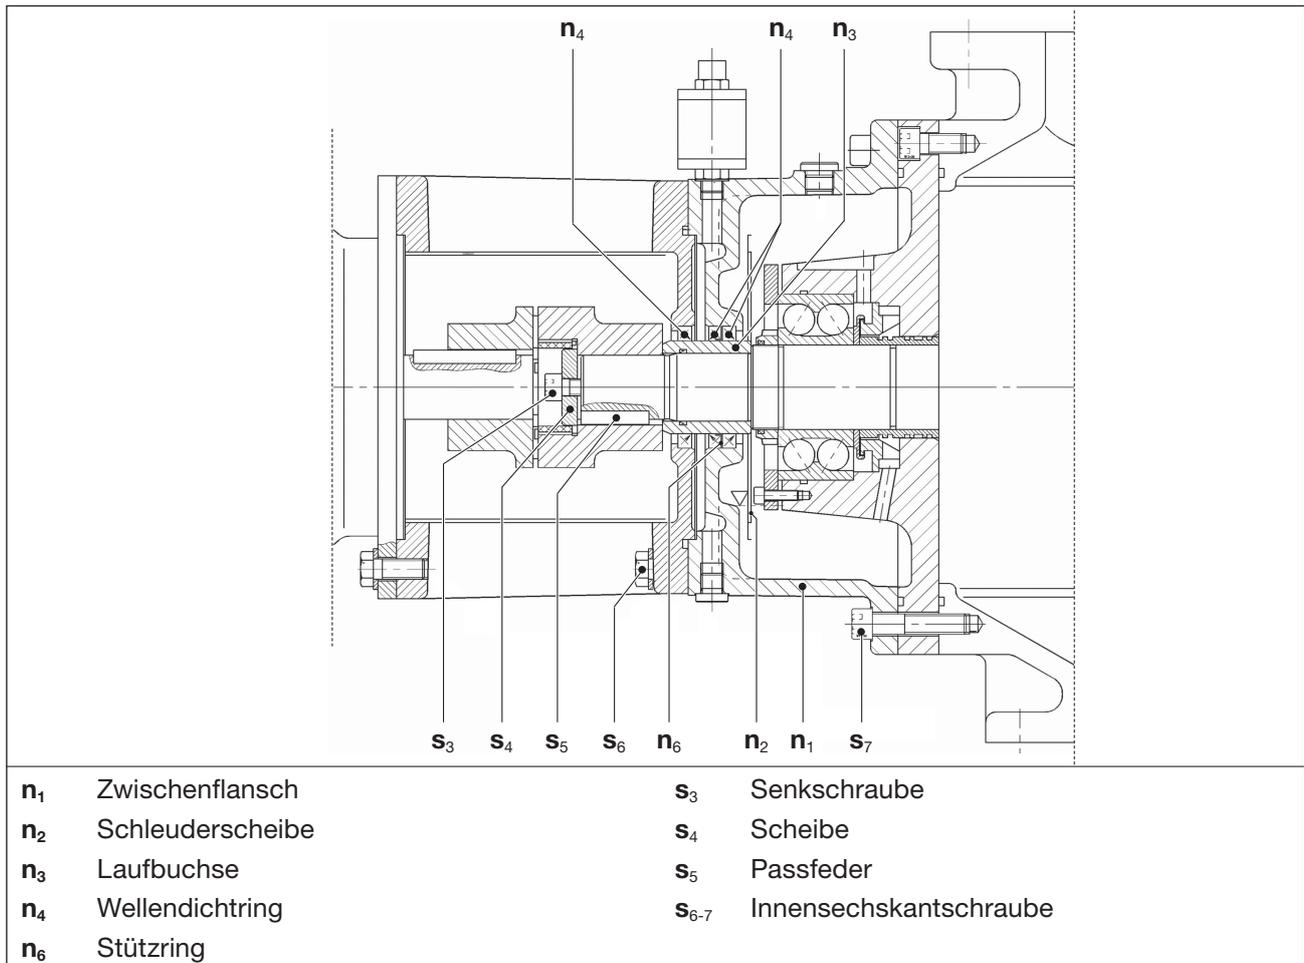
Wellendichtringe und Laufbuchse VWP 2500
